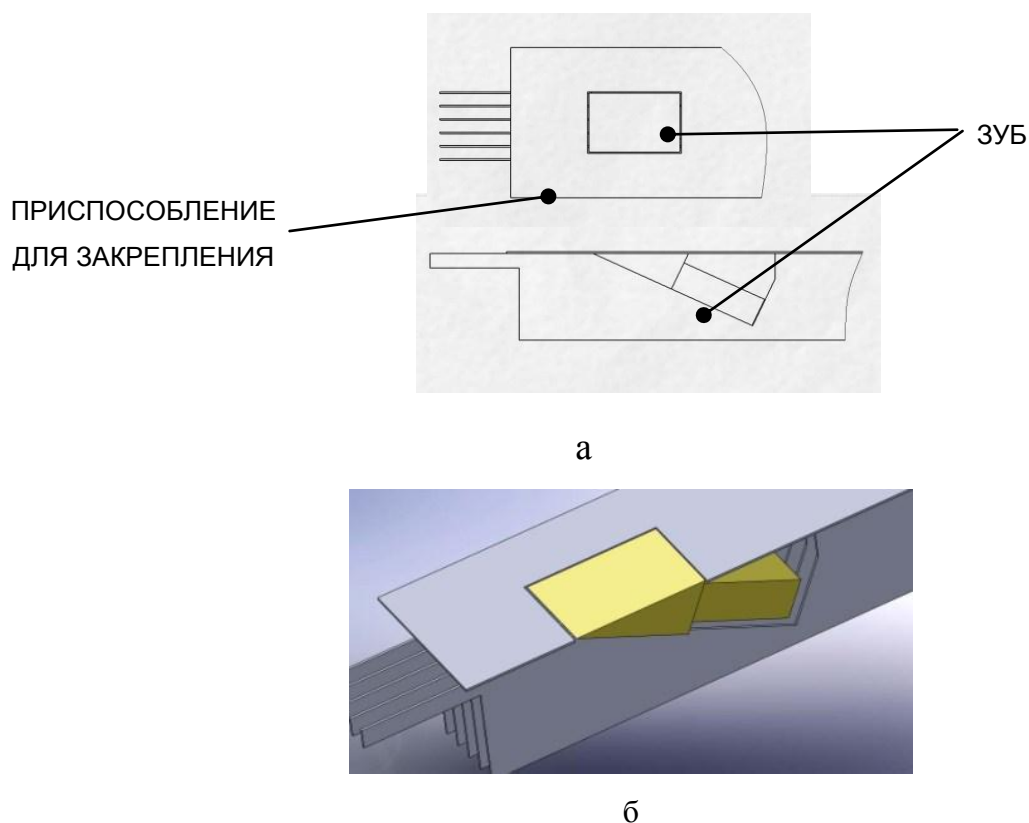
Схема (а) и общий вид (б) приспособление для термической обработки зуба экскаватора
